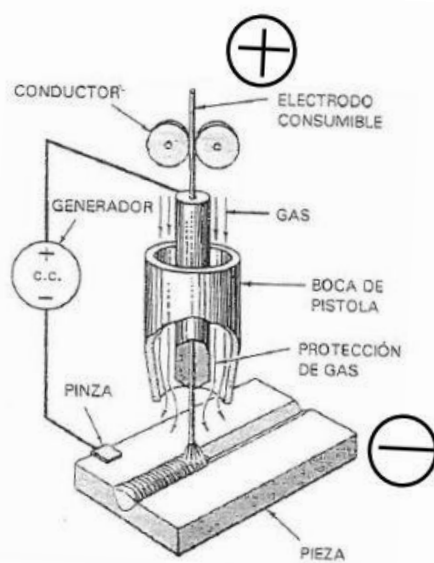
Soldadura MAG (Metal Active Gas)
